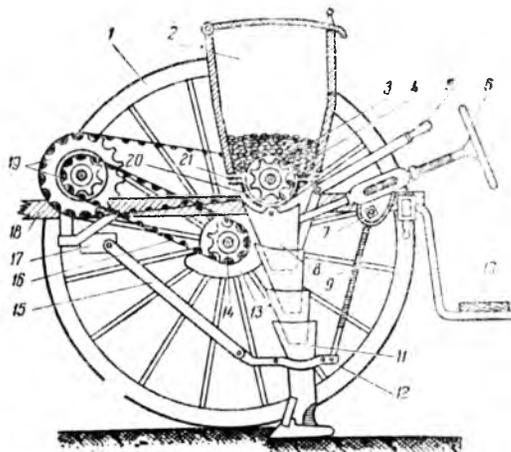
Поперечный разрез желудевой сеялки СЖ-2: 1 — ходовое колесо; 2 — бункер для семян; 3 — шестерня высевального аппарата; 4 — катушка высевального аппарата; 5 — рычаг автомата; 6 — регулятор заглубления сошников; 7 — квадратный вал подъема сошников; 8 — семяпровод; 9 — штанга сошника с нажимной пружиной; 10 — подножка; 11 — сошник; 12 — хомут сошника; 13 — автомат; 14 — шестерня на оси ходового колеса; 15 — поводок сошника; 16 — цепная передача; 17 — сошниковый брус; 18 — рама сеялки; 19 — шестерня контрпривода; 20 — кожух высевального аппарата; 21 — резиновая прокладка.
